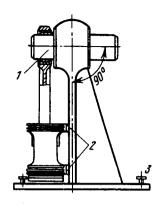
Приспособление для проверки перпендикулярности оси нижней головки шатуна к образующей поршня:
